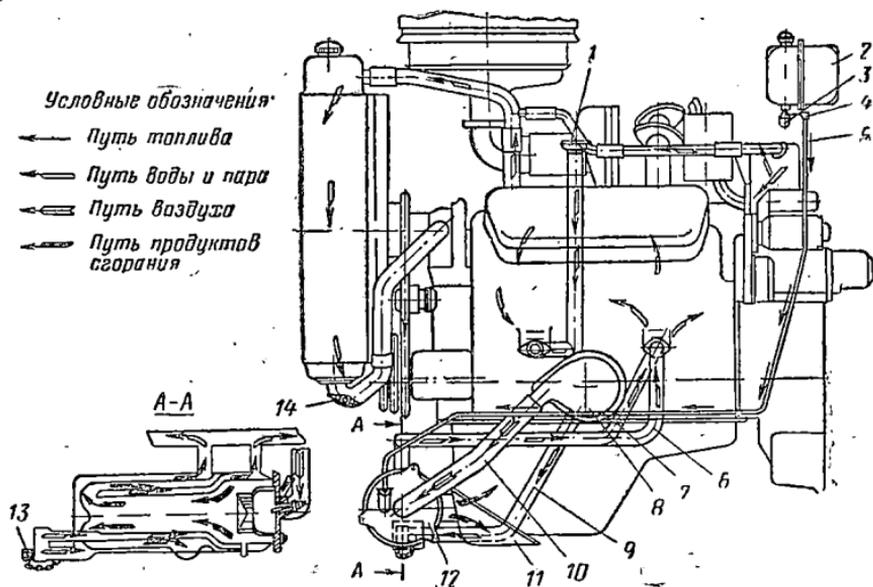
Схема предпускового подогрева двигателей СМД-60, СМД-62:
